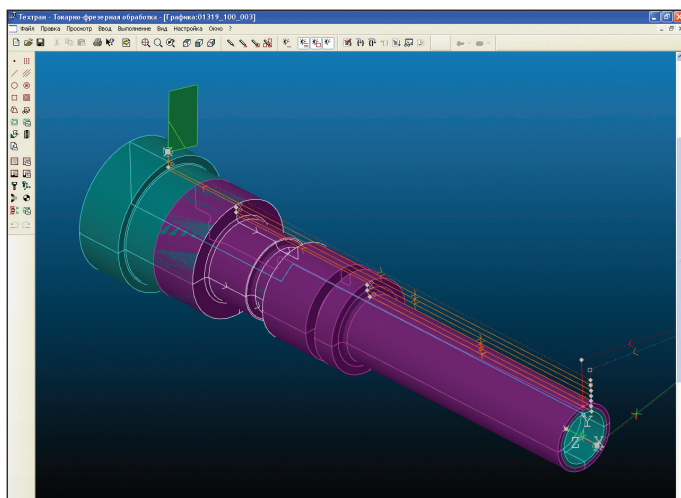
Токарная деталь и заготовка (произвольный вид)
